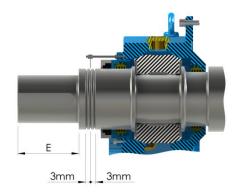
Выравнивание вала с подшипниками скольжения
